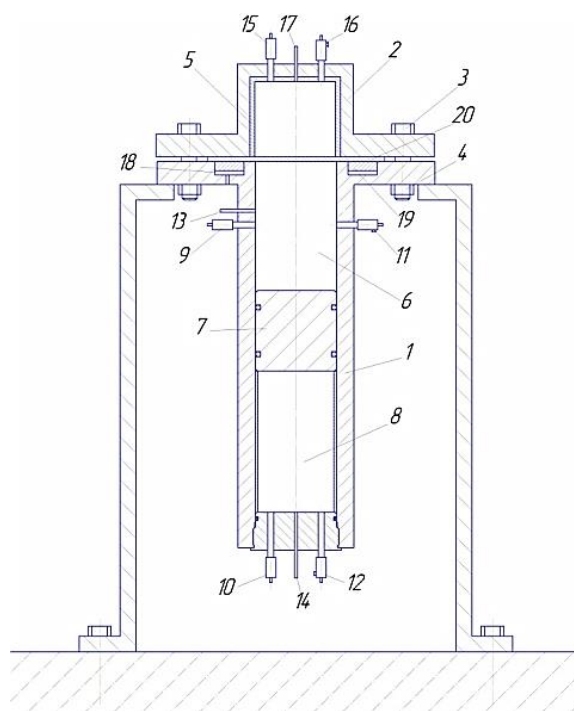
Схема устройства газовой штамповки с поршневым мультипликатором давления
